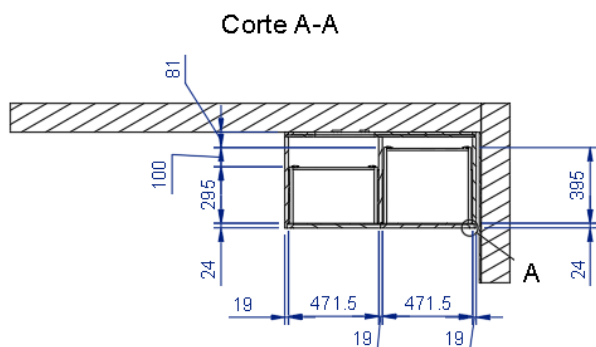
Desenho técnico de um corte que demonstra a profundidade das gavetas.
